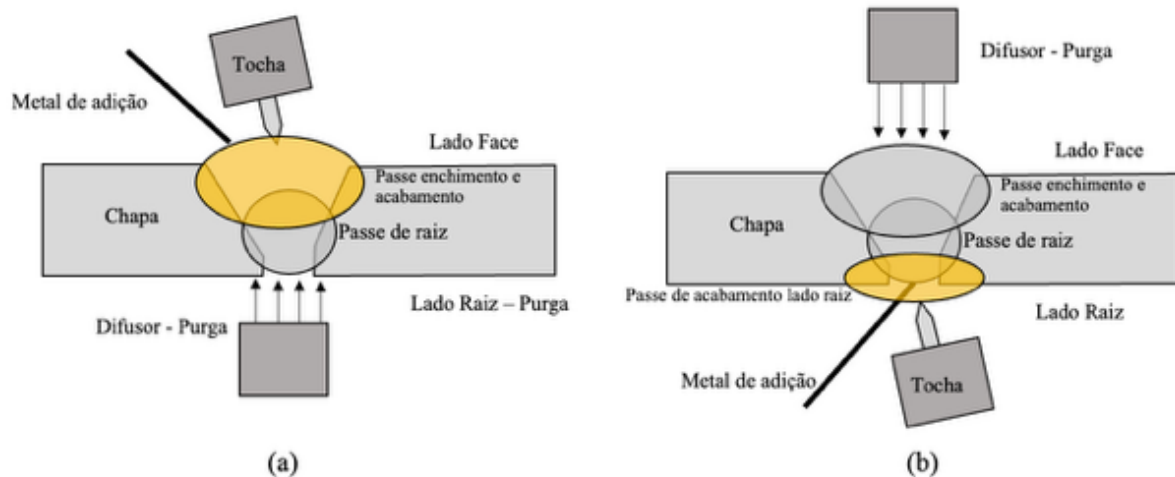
Soldagem de enchimento e acabamento das chapas CP2A e CP2B com o processo GTAW.
